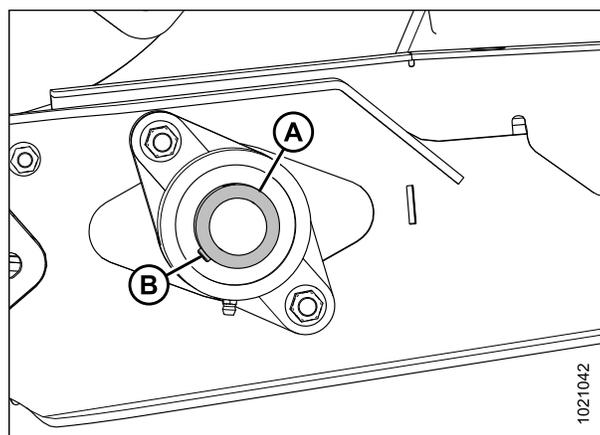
Подшипник приводного ролика подающего полотна
